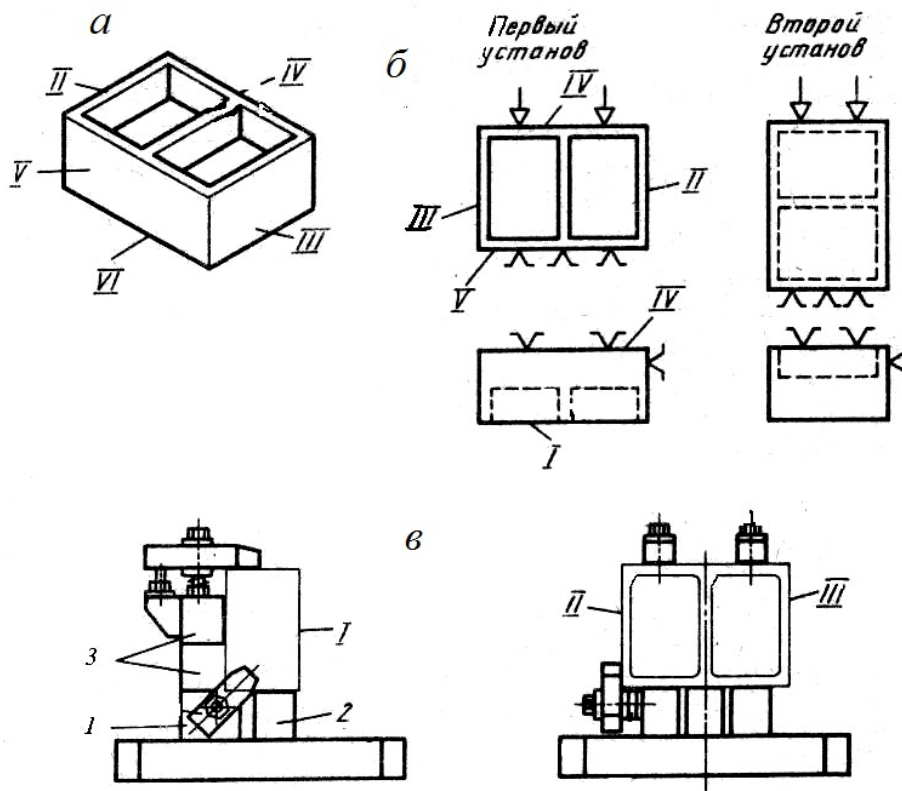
Базирование заготовок с использованием откидного упора и компоновка приспособления:
